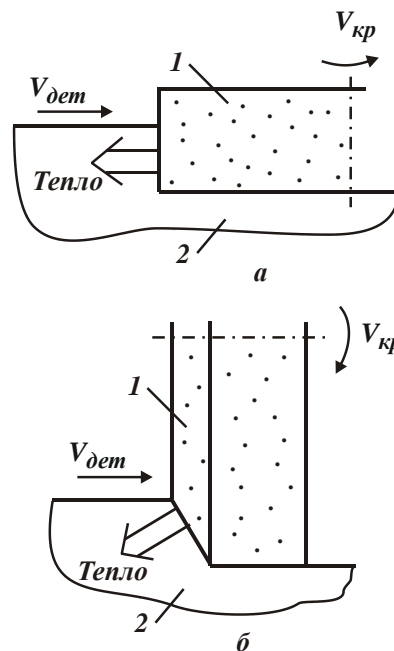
Расчетные схемы шлифования: а – торцом круга и б – периферией круга: 1 – шлифовальный круг; 2 – обрабатываемая деталь
